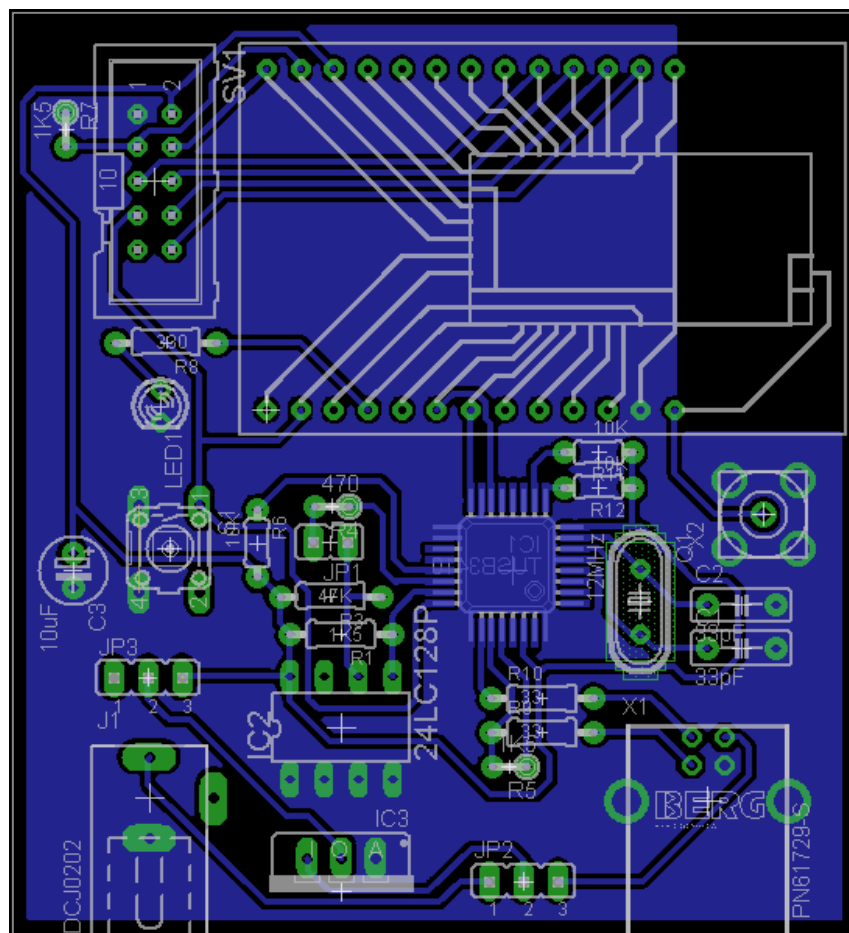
PCB do Coordenador (Dimensão: 6.25cm x 6.9cm).
